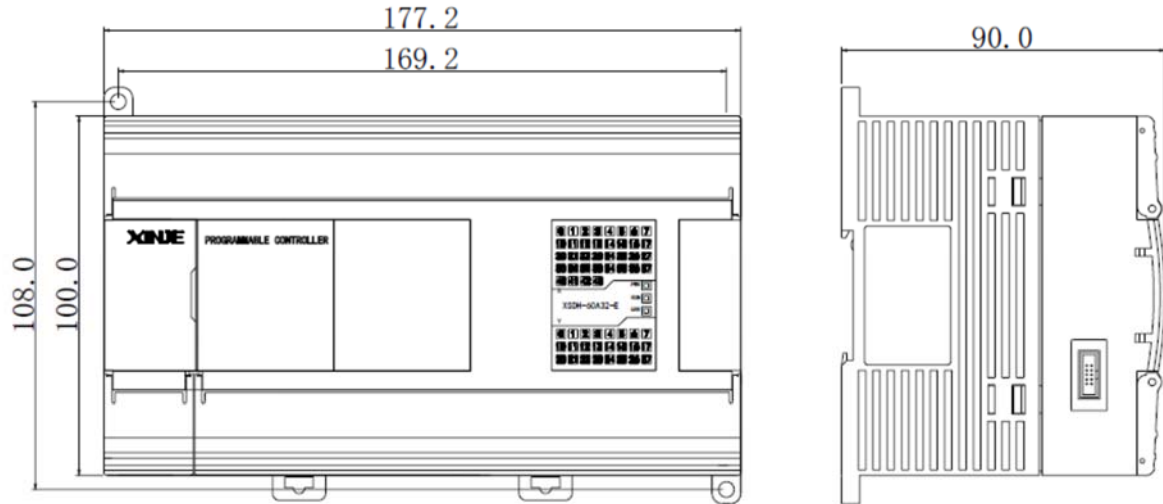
Габаритные и установочные размеры XSDH-60A32-E
